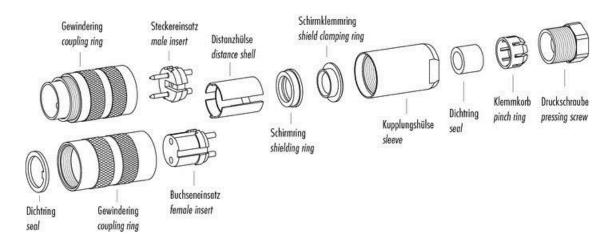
Explosionszeichnung des E/A Steckverbinders
